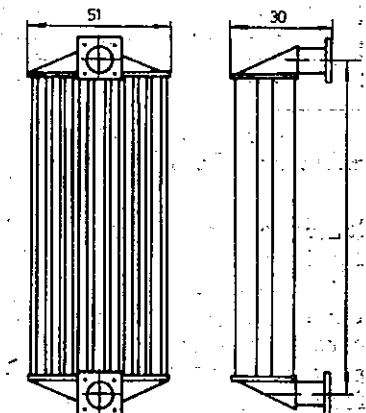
Radiatoare cu țevi drepte. Dimensiunile sînt în cm.
